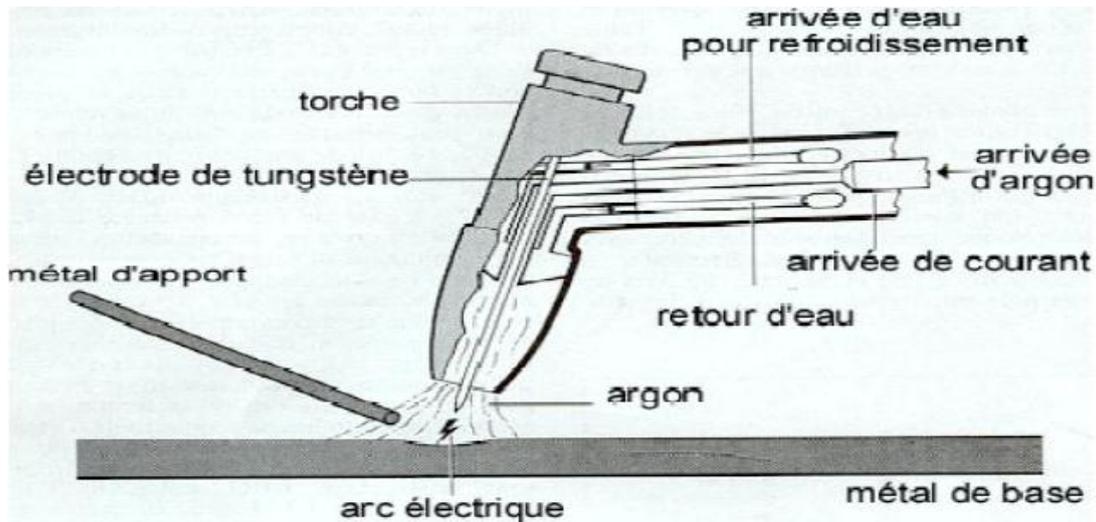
procédé de soudage TIG sous protection d'argon
